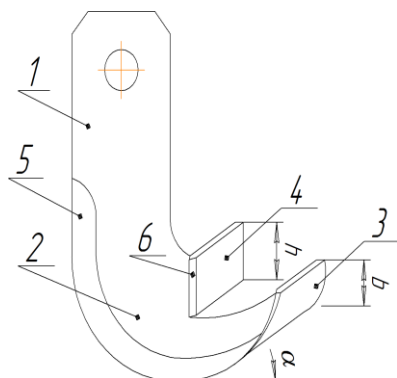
Усовершенствованный L-образный нож: 1 – стойка ножа; 2 – крыло; 3 – отогнутая часть крыла; 4 – рыхлитель; 5,6 – режущая часть
